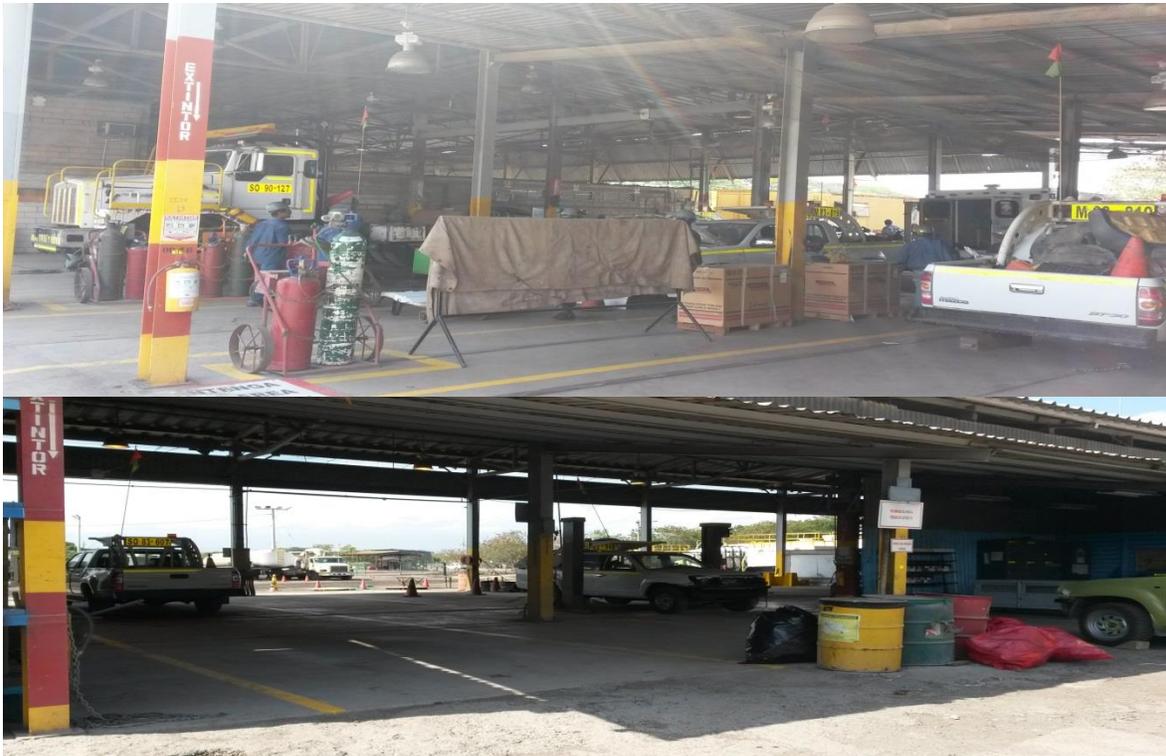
Taller de latonería, soldadura y pintura. *Fuente: autor
